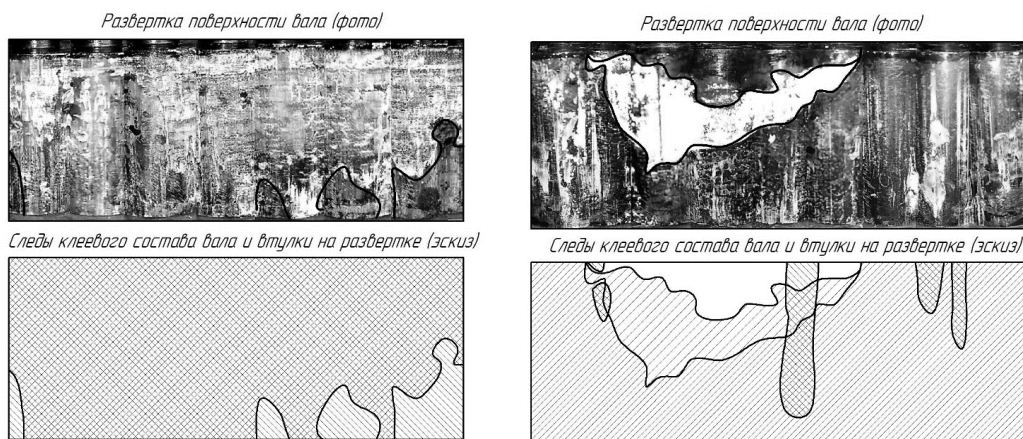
Развертки клеевых соединений (клей Efele 126, слева – сборка с направленным формированием, справа – ручная сборка)
